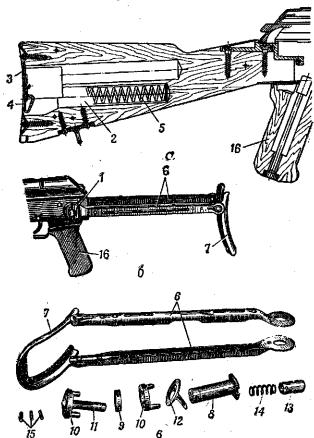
Приклад и пистолетная рукоятка: a — деревянный приклад; 6 — складывающийся приклад: b — складывающийся приклад в разобранном виде; l — антабка для ремня; 2 — гнезло для принадлежности; 3 — затыльник; 4 — крышка; 5 — пружина для выталкивания пенала с принадлежностью; 6 — тяги; 7 — плечевой упор; 8 — сединительная втулка; 9 — гайка; 10 — фиксаторы приклада; 11 — соединительный стержень; 12 — шайба с антабкой; 13 — колпачок; 14 — пружина; 15 — шпильки; 16 — пистолетная рукоятка
